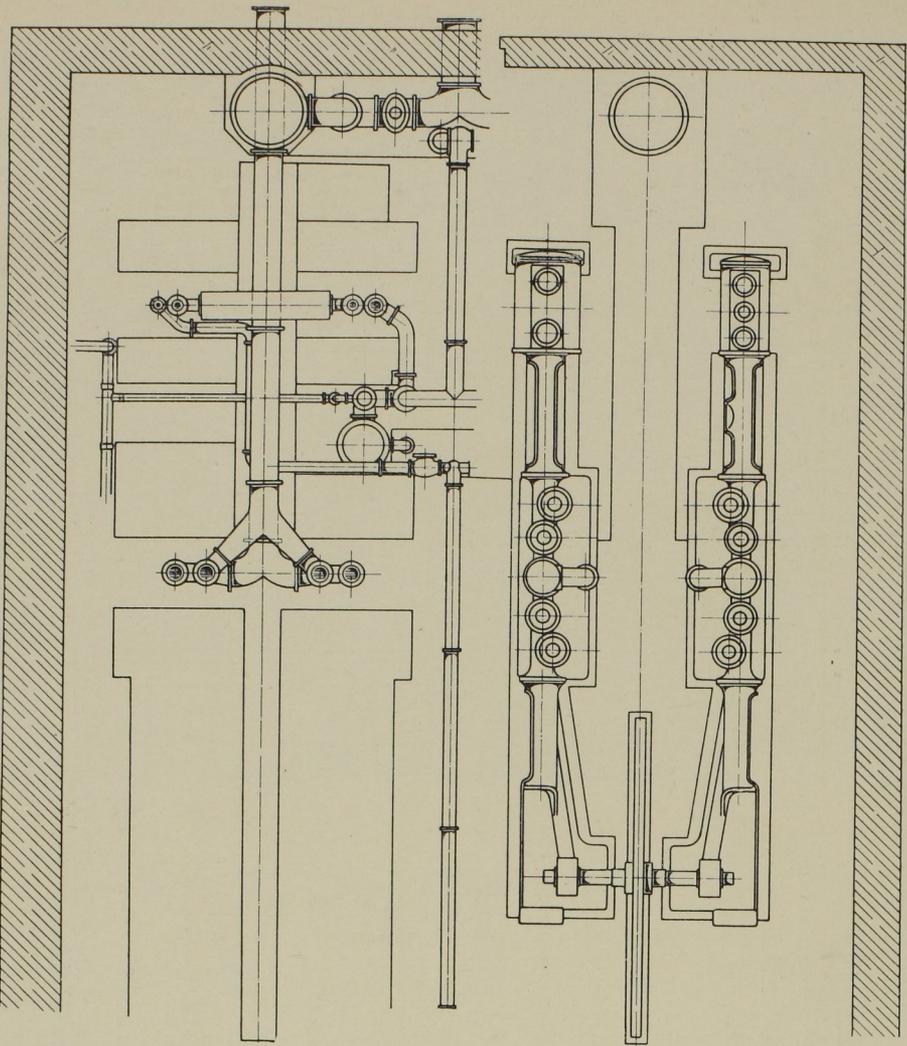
Grundriss der Maschine und Rohrplan. Massst. 1:120. Wasserwerk Stuttgart-Bergstrasse.
